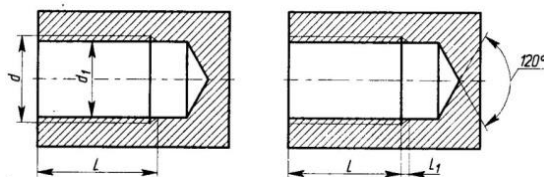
Длина резьбы:  $d$  – наружный диаметр;  $d_1$  – внутренний диаметр;  $L$  – длина резьбы;  $l_1$  – сбег
